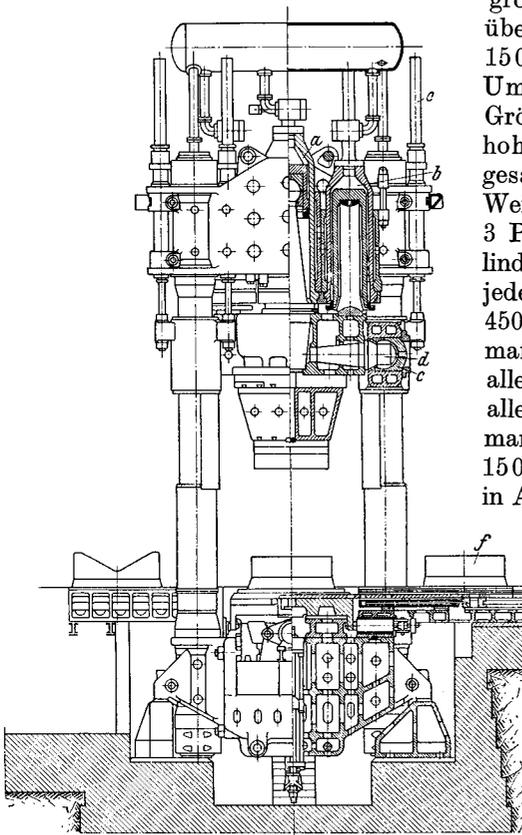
Schnitt und Ansicht durch eine dampfhydraulische Schmiedepresse mit 15000 t Druckvermögen (Schloemann, Düsseldorf).
